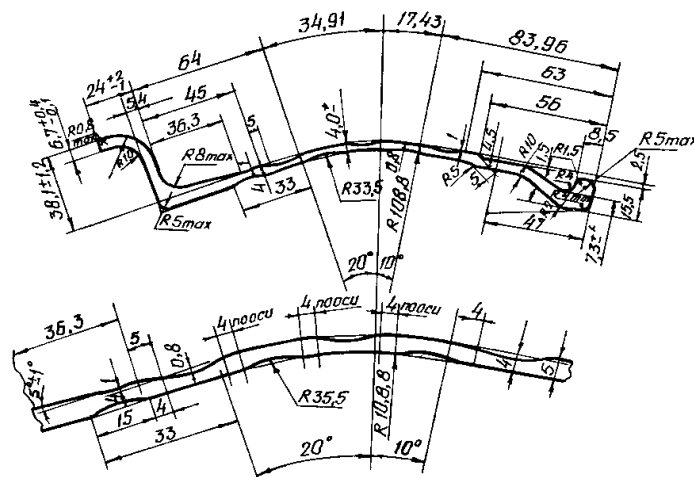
Рабочий чертеж профиля 7.0-20-05
